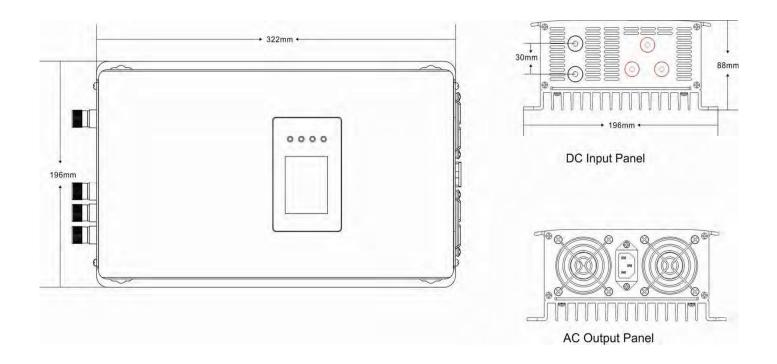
SUN-1000G2-WAL-Umrisszeichnung
